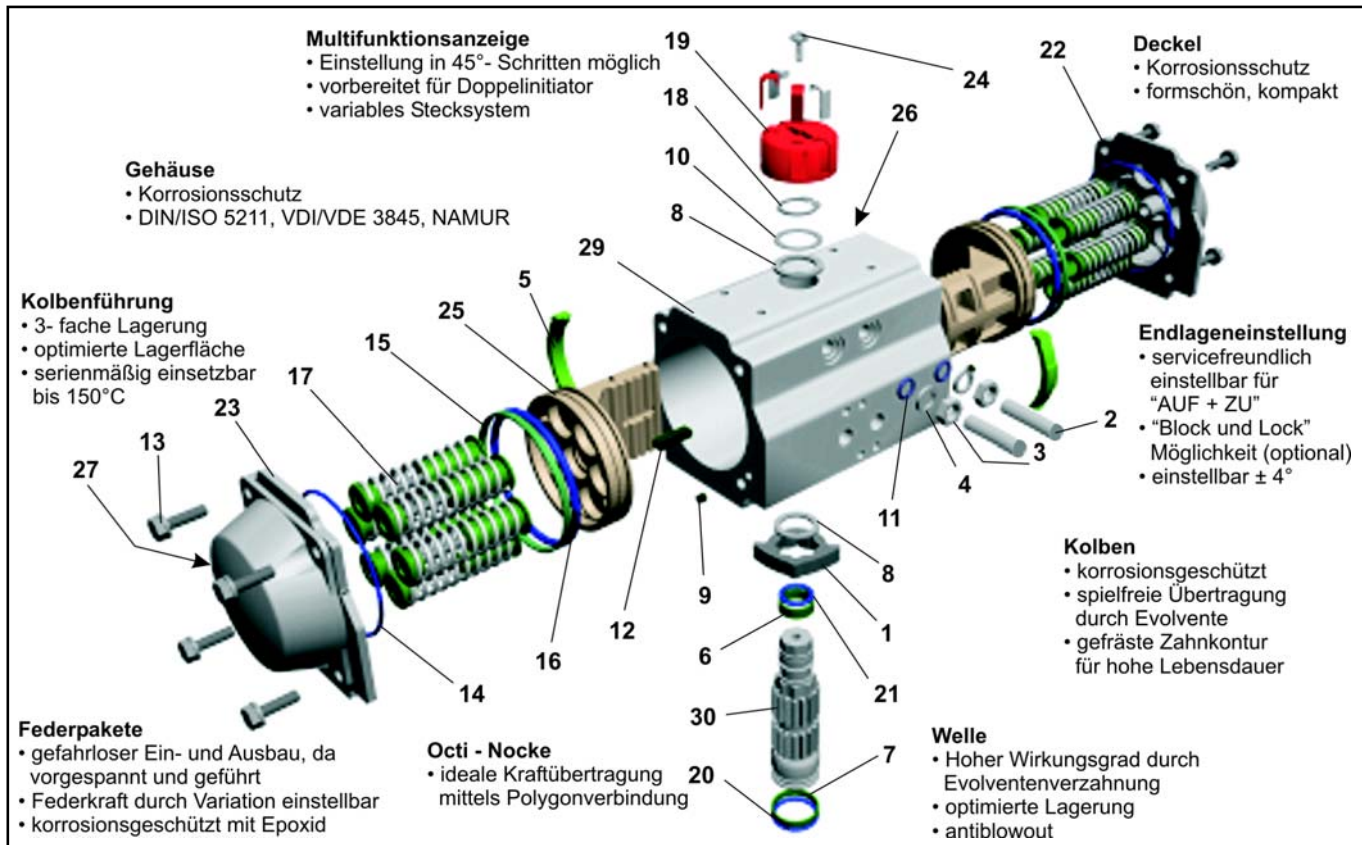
Explosionszeichnung des Schwenkantriebes BR 31a
